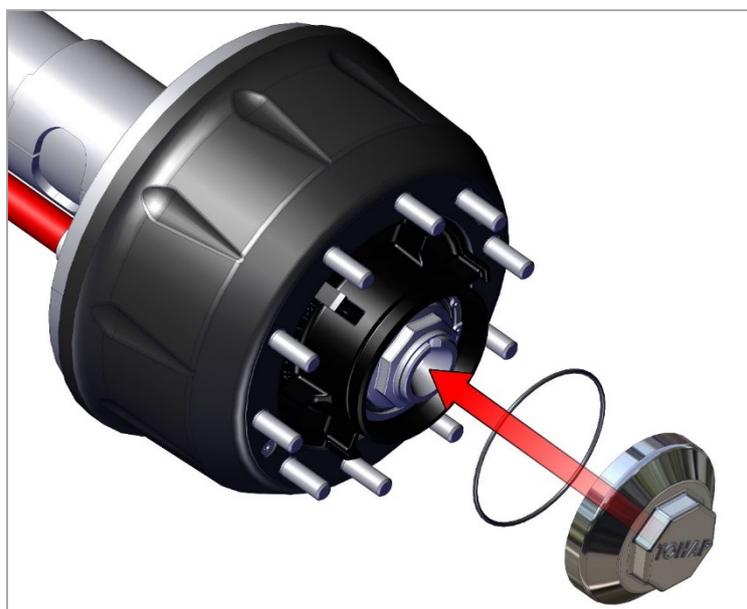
Монтаж крышки ступицы колеса с резиновым уплотнительным кольцом.
